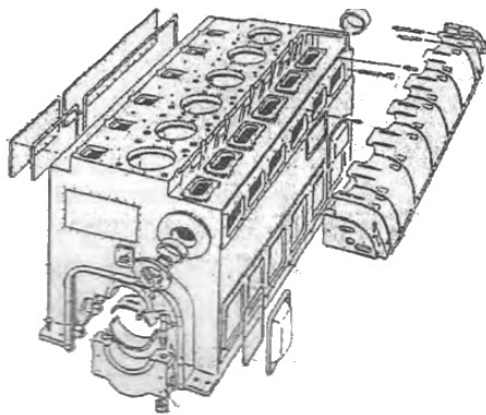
Моноблок станины и блока цилиндров дизеля 6L23/30 MAN-B&W
